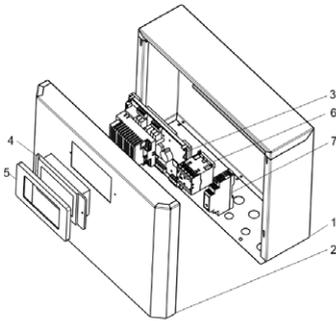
Aufbau des Innengerätes der Wärmepumpe
